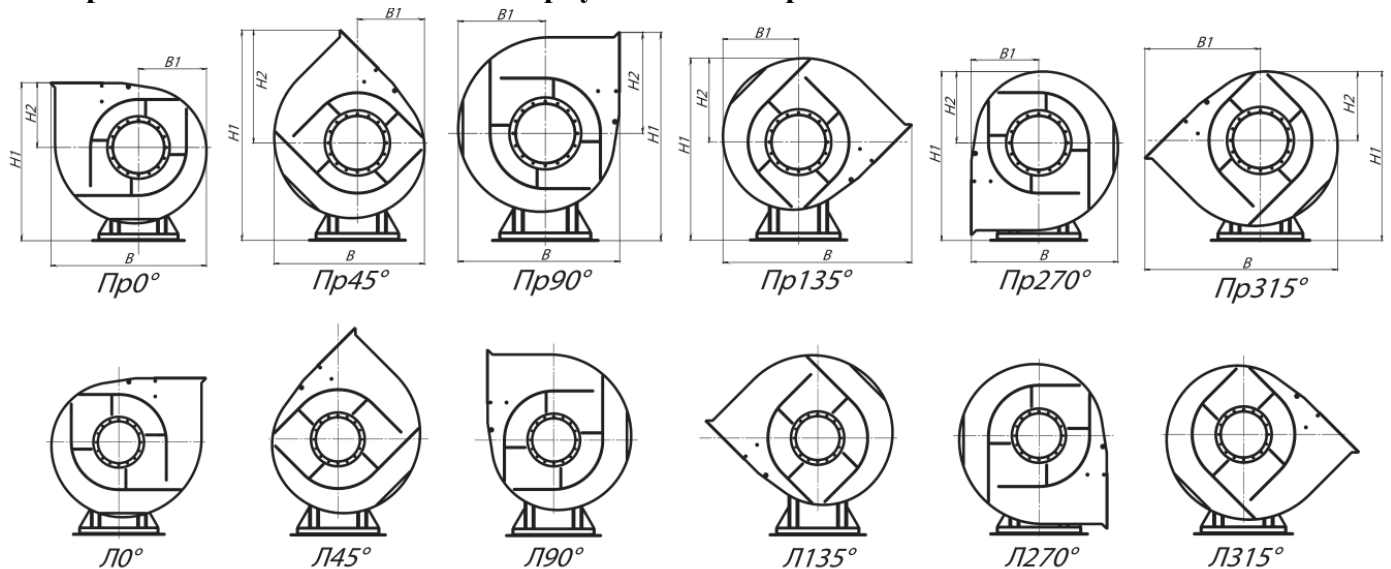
размеры, зависящие от положения корпуса вентилятора
